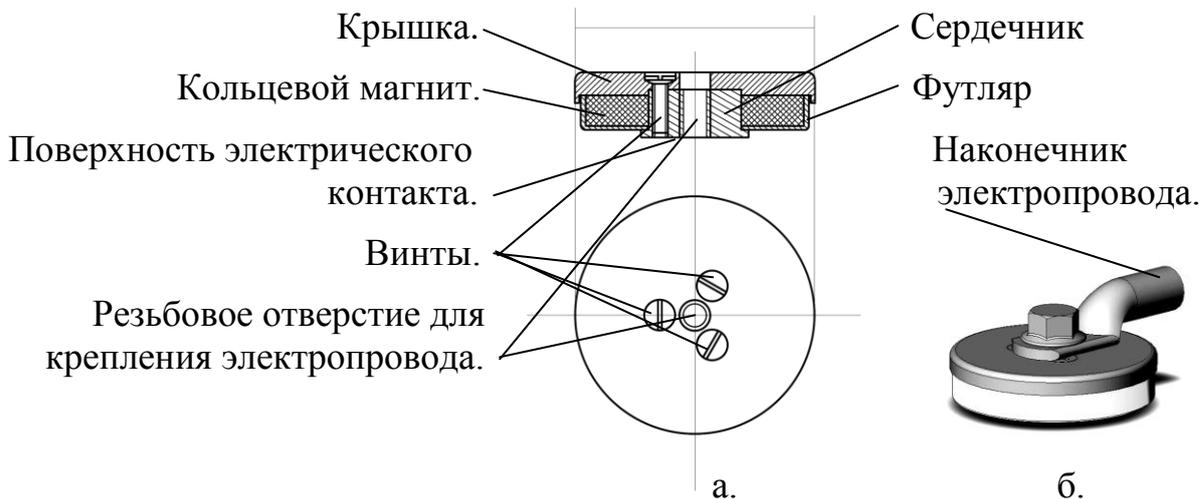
а – конструкция, б – магнитный контакт (в сборе).
